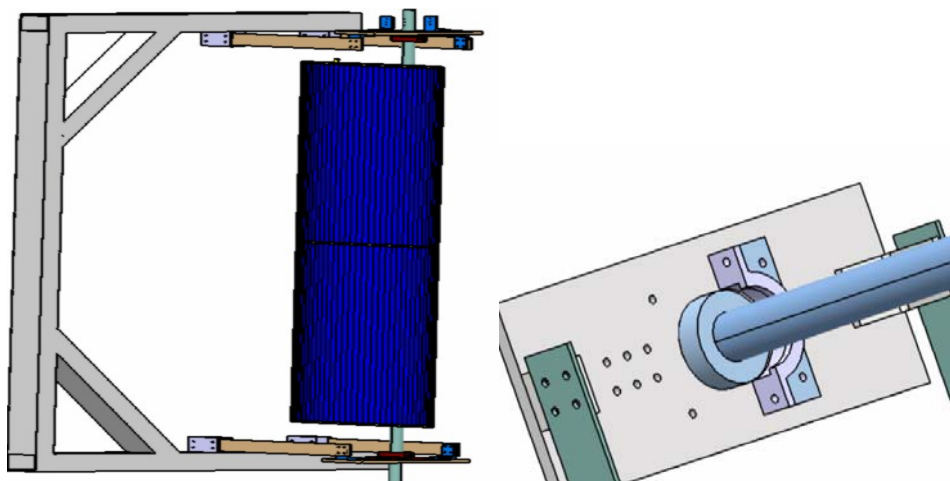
(a) Dispositivo desenhado (b) Detalhes da junção da flange e rolamento
